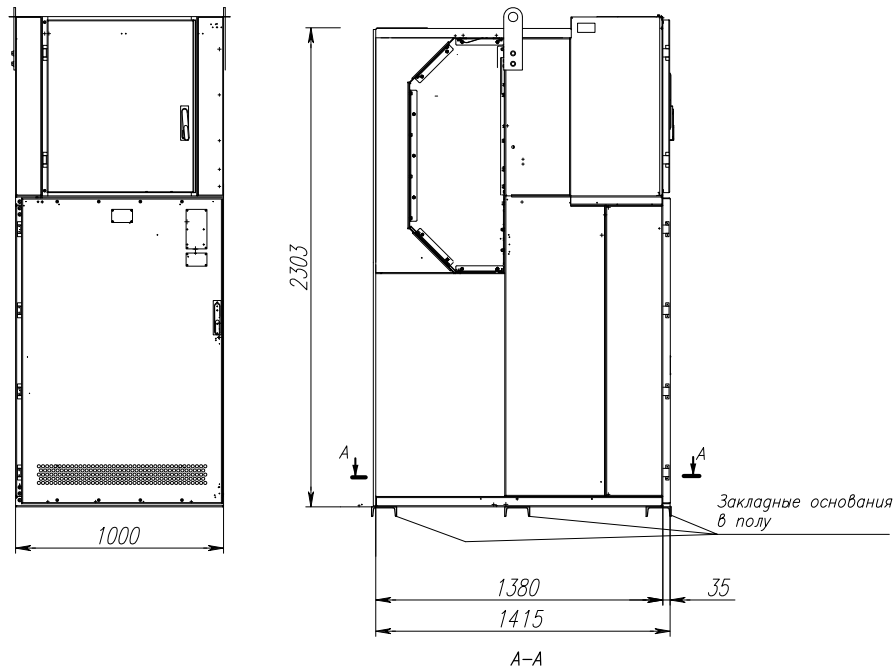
Общий вид и габаритные размеры шкафа с ТСН 63 кВА
